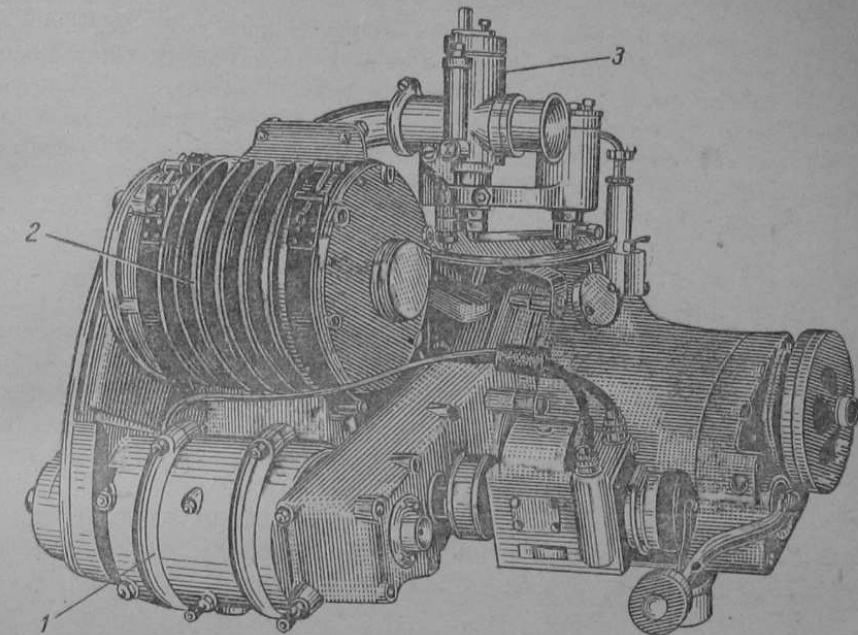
Установка нагнетателя сверху двигателя мотоцикла ГК-1:
